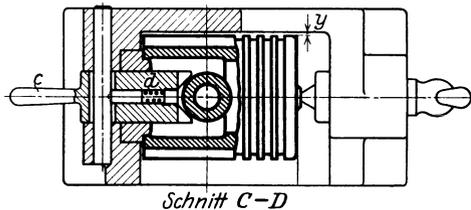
Standbohrspannvorrichtung mit doppelter Werkzeugführung.
